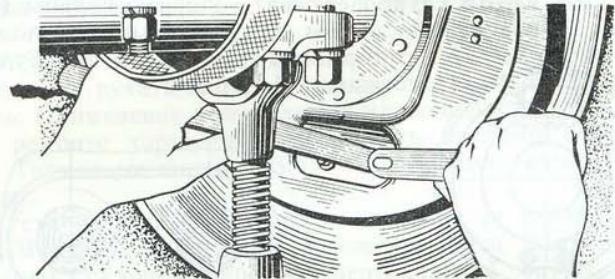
Регулировка опорных пальцев тормозных колодок заднего колеса
